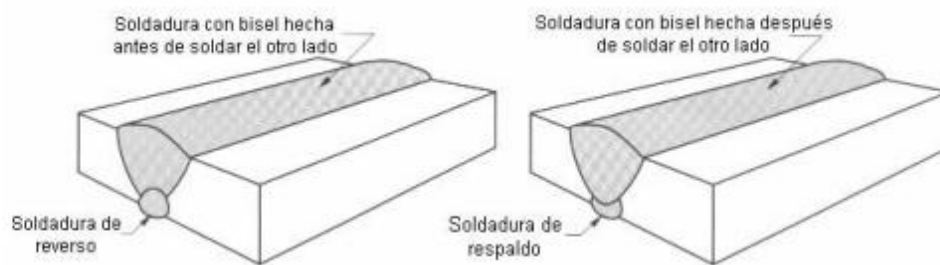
Izquierda: Soldadura de reverso; Derecha: Soldadura de respaldo.
